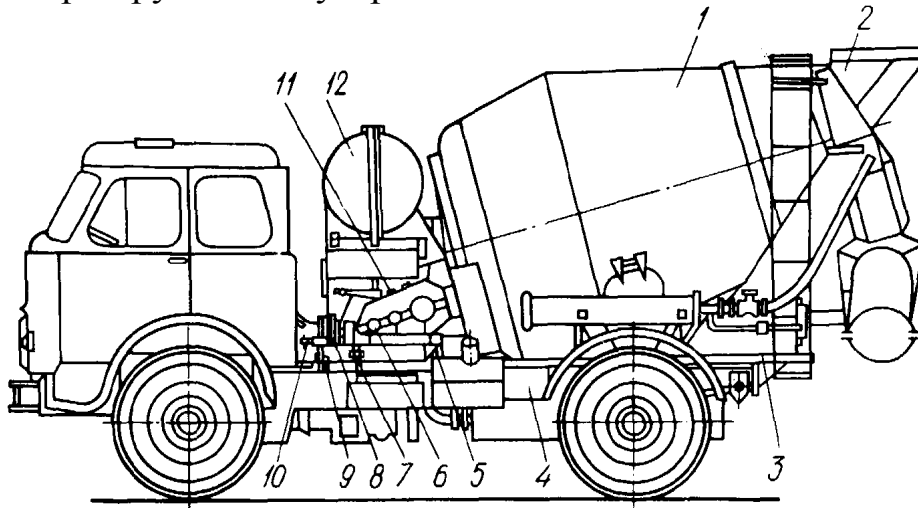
Автобетоносмеситель СБ-69Б: 1 – барабан; 2 – загрузочно-разгрузочное устройство; 3 – рама; 4 – шасси; 5 – контрольно-измерительные приборы; 6 – привод; 7 – муфта; 8 – 11 – механизмы управления подачей топлива с муфтой сцепления, редуктором и декомпрессором; 12 – бак для воды
